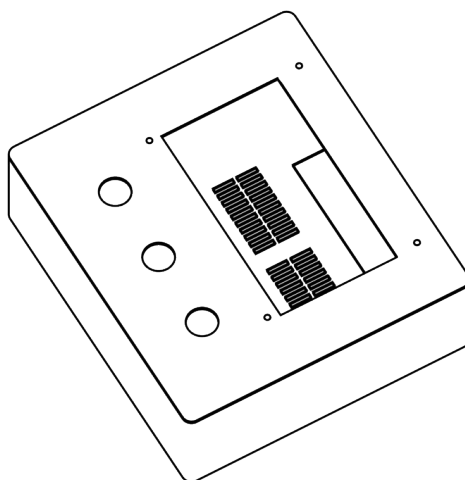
Корпус микрокомпьютера и дисплея
